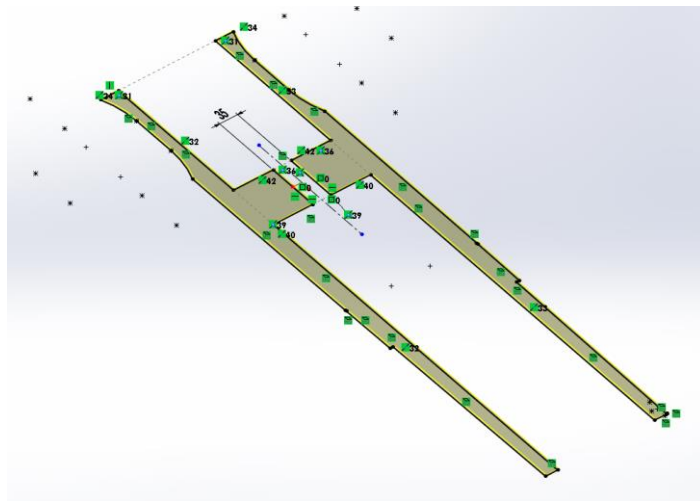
Croquis pletina refuerzo superior bastidor.
